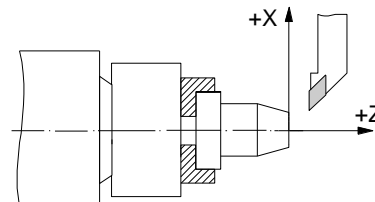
Система координат заготовки, що рекомендується, при фрезерній обробці
